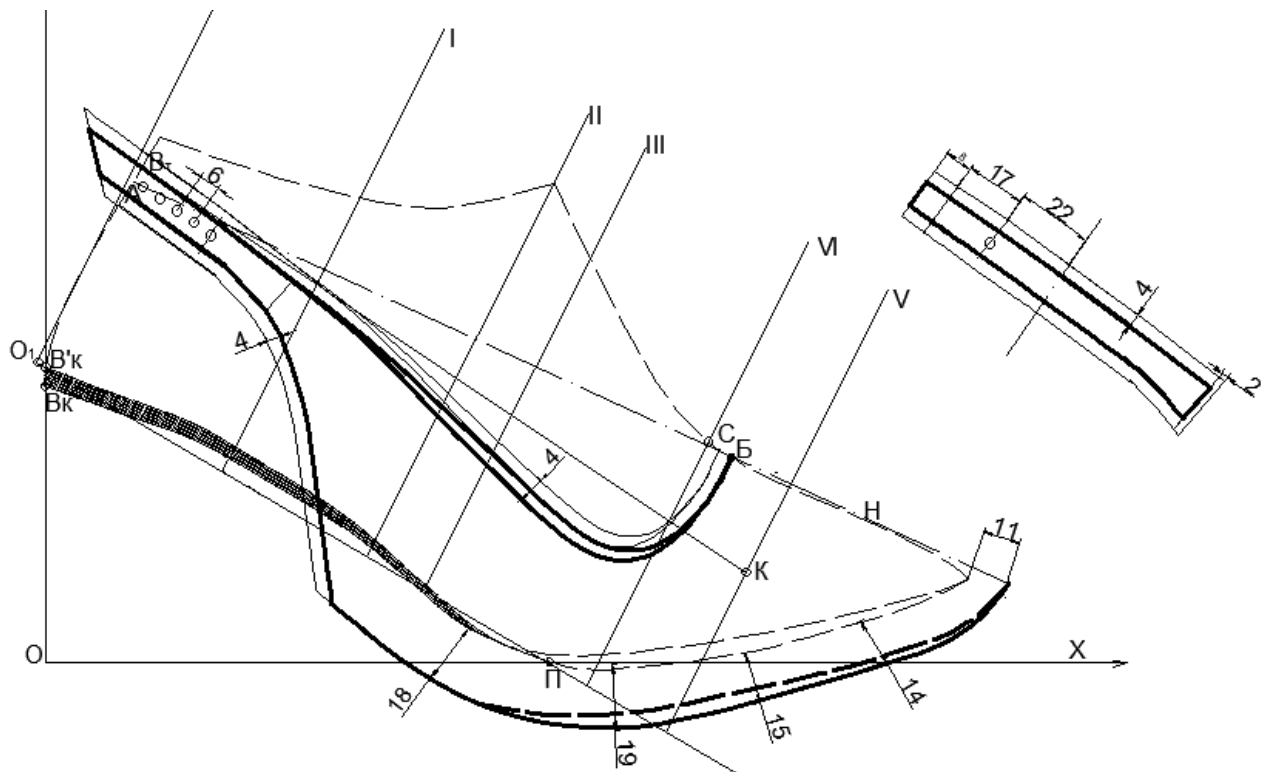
Побудова зовнішніх деталей верху.
